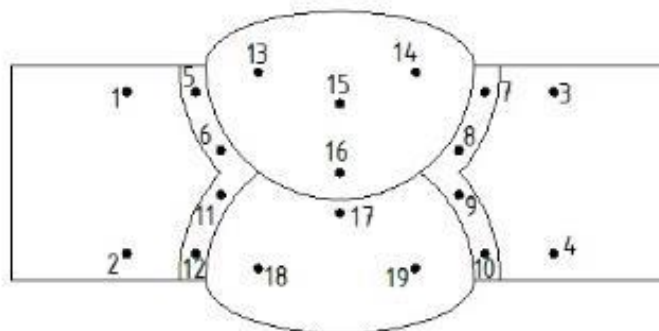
Схема замера твердости сварных образцов
